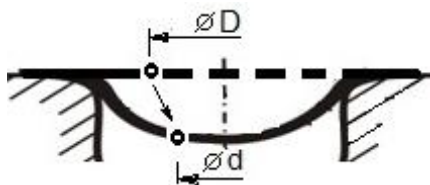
Схема перемещения материальной точки заготовки при штамповке дна
